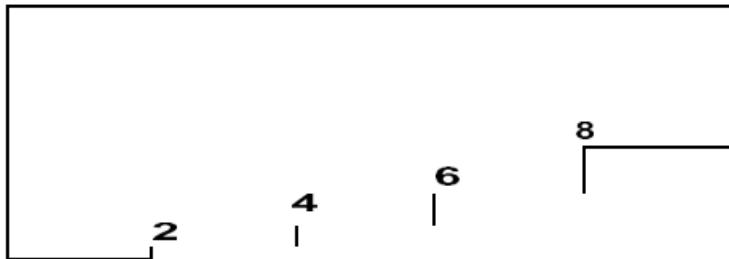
Контрольный образец с разновысотными ступеньками
